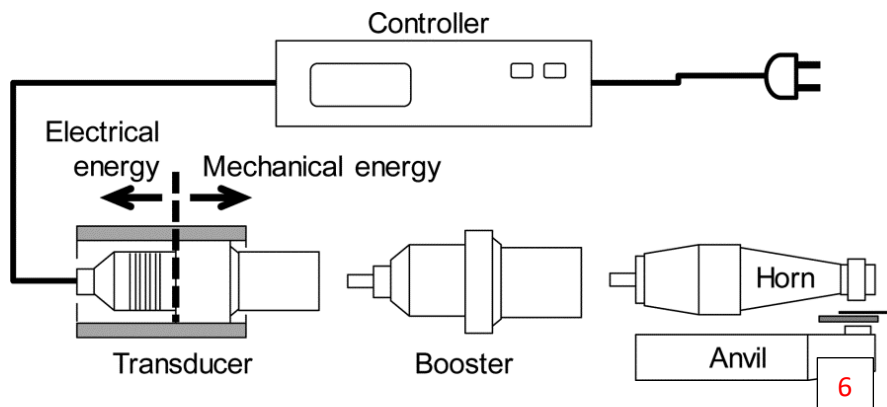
Componentes da zona de soldadura: (6) bigorna [14]
